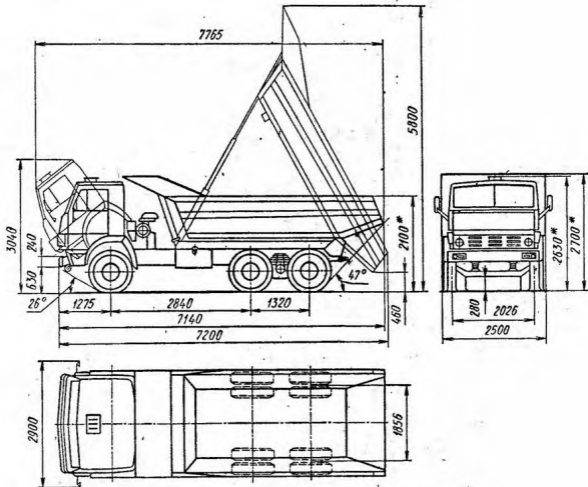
Габаритные размеры самосвала КамАЗ-5511
